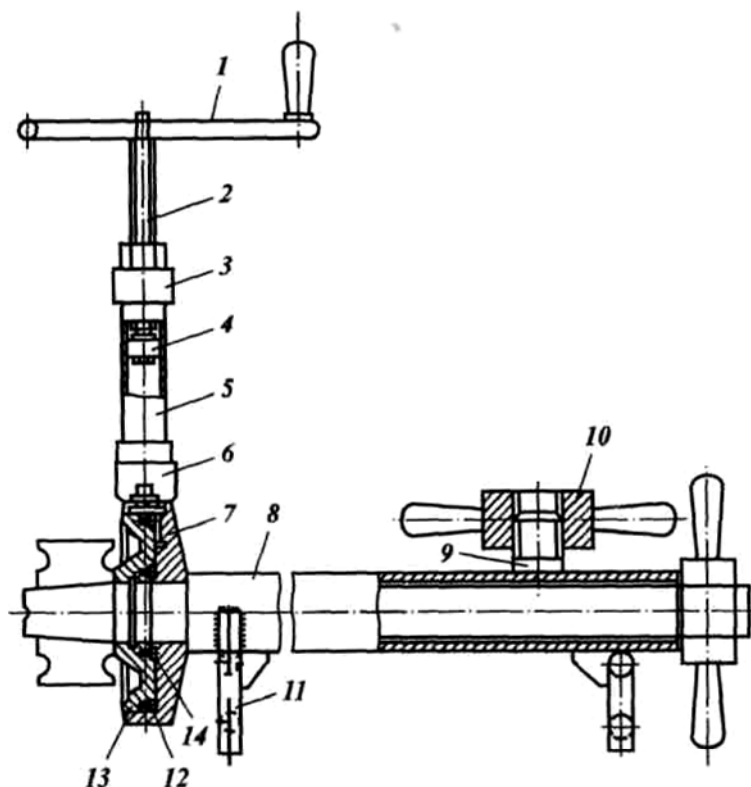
Гидравлический съемник поршней буровых насосов: 1 - маховик; 2 - винт; 3 - крышка цилиндра; 4 - поршень; 5 - цилиндр; 6 - муфта; 7 - корпус; 8 - труба; 9 и 11 - стойки; 10 - рукоятка; 12 и 14 - уплотнения; 13 – поршень
